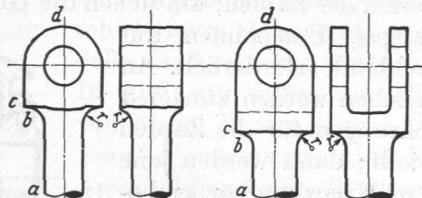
und 226. Richtige Gestaltung von Stangenköpfen. (Durch Drehen und Fräsen bearbeitbar.)
